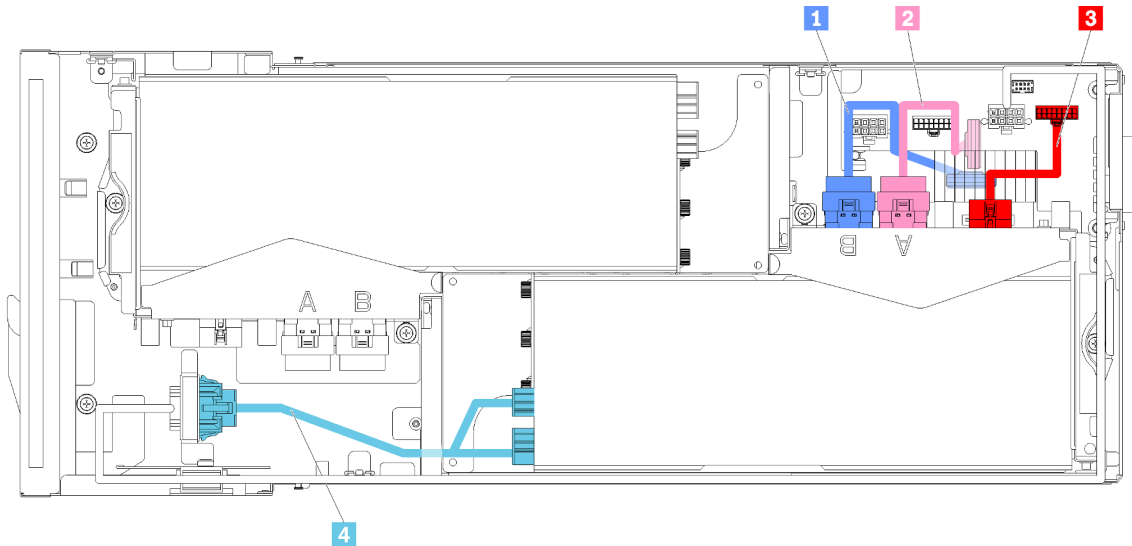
Câbles de l'assemblage de cartes mezzanines arrière
